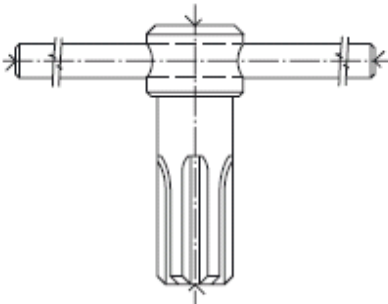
Werkzeug Nr. A – Führungsbüchsen-Schlüssel
